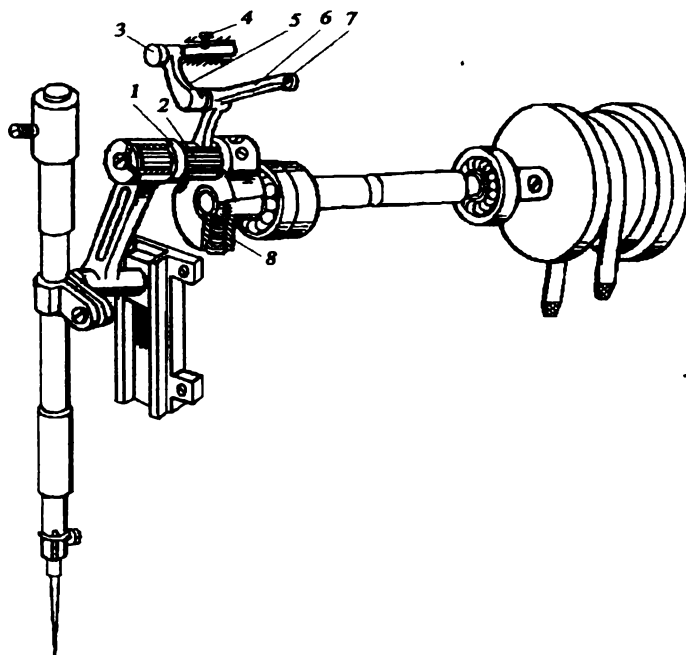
Механизм движения иглы и нитепритягивателя машины 1022-М кл. ОЗЛМ
